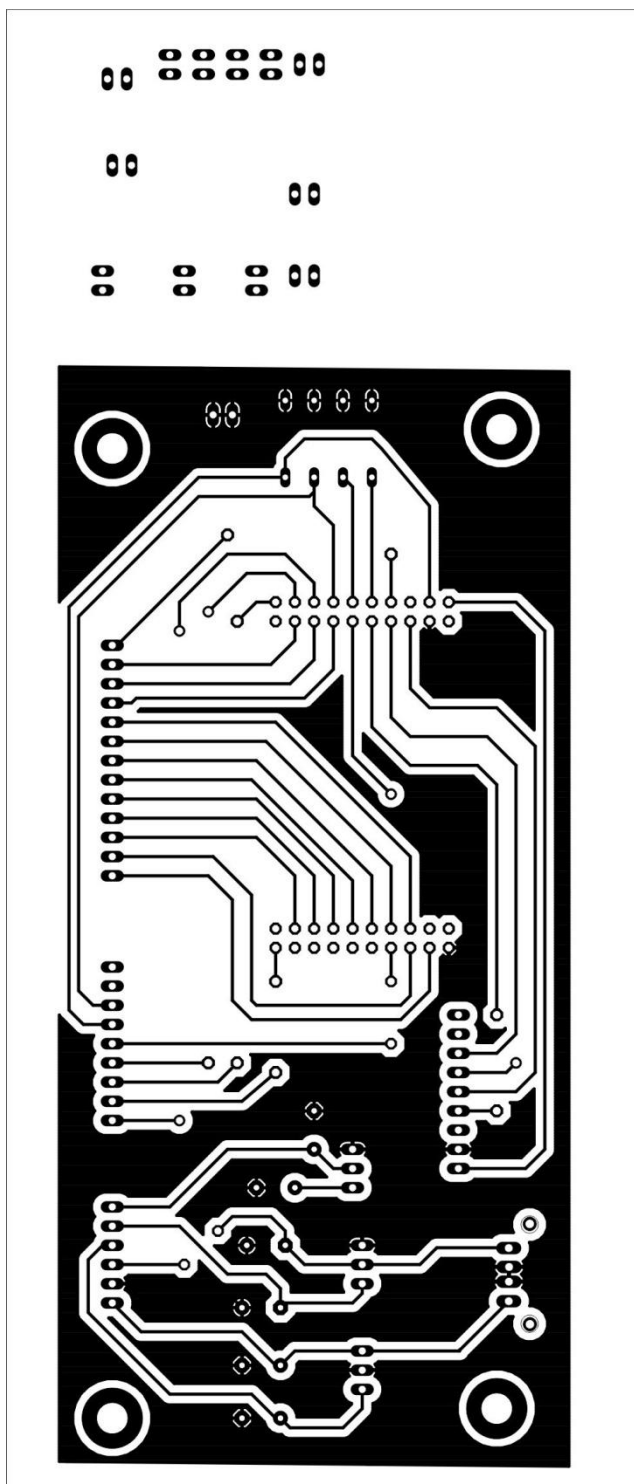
Layout PCB del Sistema analógico (CAPA1)
